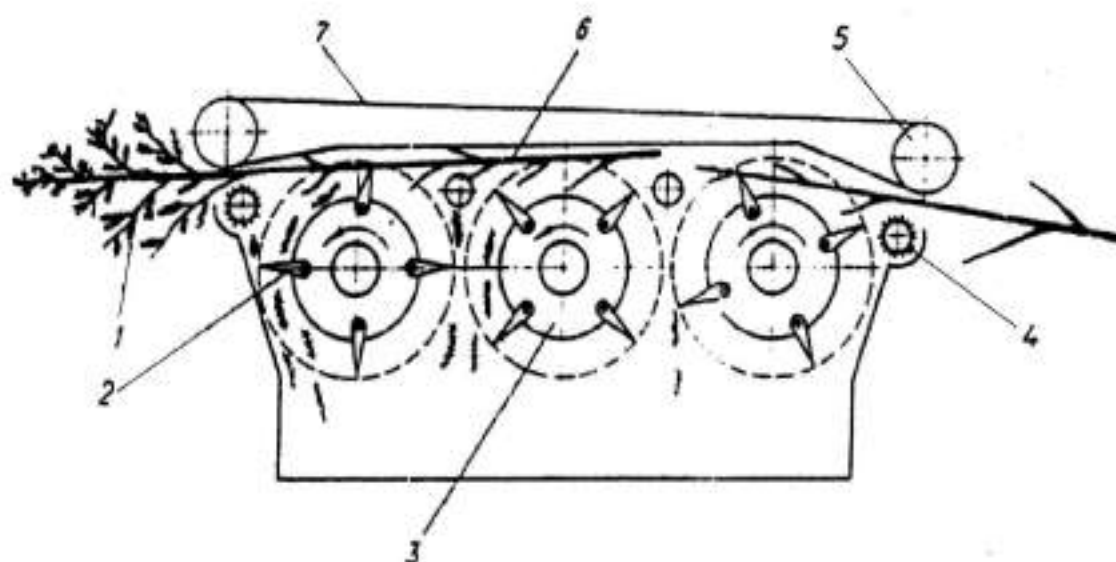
Механічний пристрій для відділення хвої ОДЗ-3,0: 1 - гілка; 2 – ножі; 3 – барабан; 4, 5 – притискні вальці; 6 – опорні вальці; 7 – транспортер [3]
